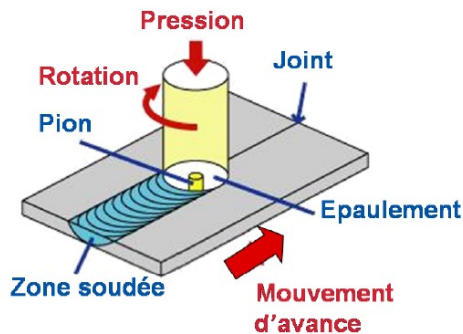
Principe du soudage par friction malaxage conventionnelle [15]
